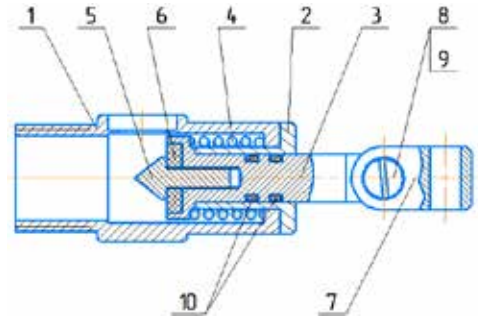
Корпус клапана в сборе резаков ФЛЦ-РК и ФЛЦ-РКФ
